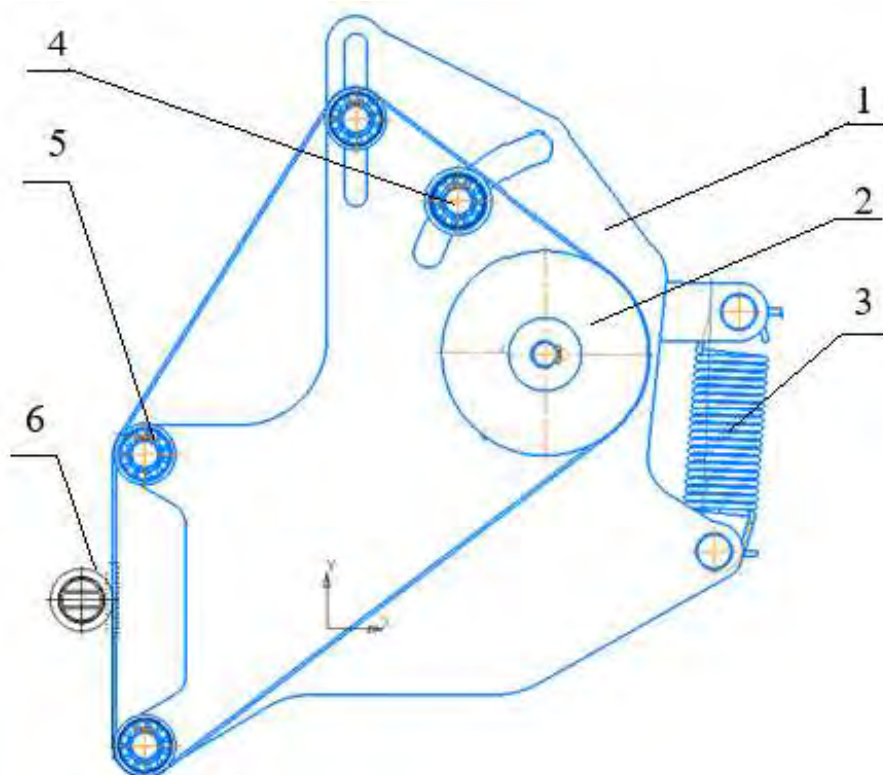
Компоновка приспособления: 1 – корпус, 2 – приводной ролик, 3 – механизм натяжения, 4 – натяжной ролик, 5 – опорный ролик, 6 – заготовка
